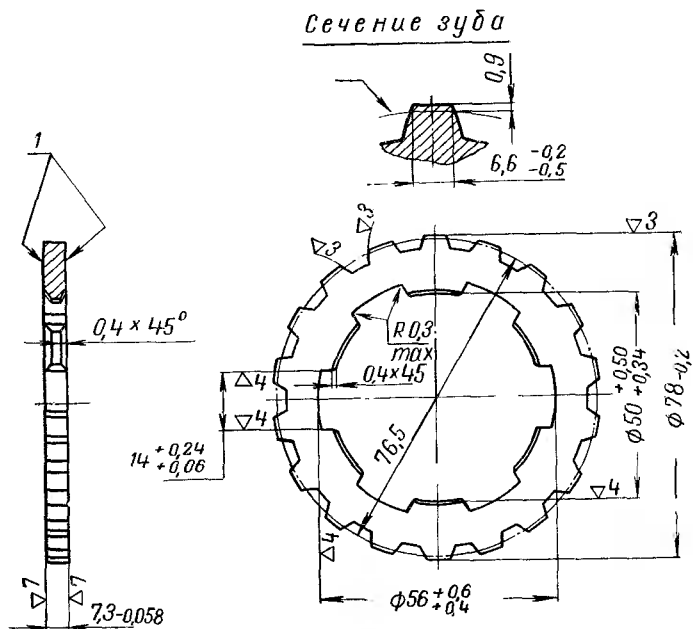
Шайба упорная шестерни пятой передачи ведомого вала
